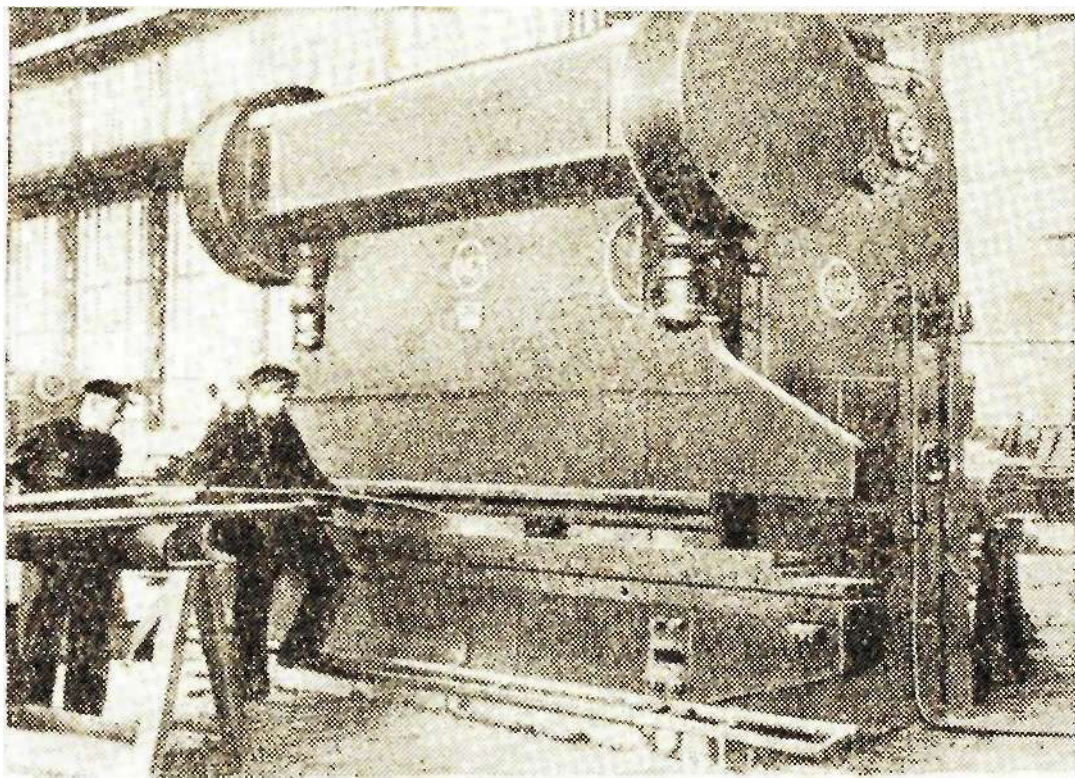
Продольно-гибочный пресс для холодной штамповки деталей из листовой и широкополосной стали
